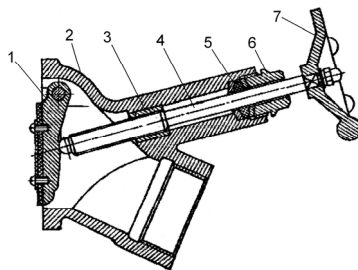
Напорная задвижка коллектора насоса:
